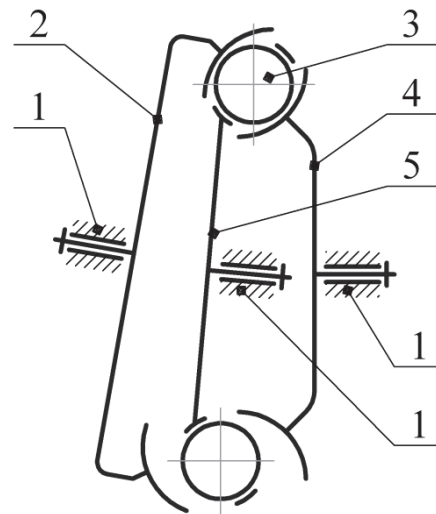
Кинематическая схема конической передачи с ПТК: 1) стойка; 2) колесо; 3) тело качения; 4) колесо; 5) сепаратор
